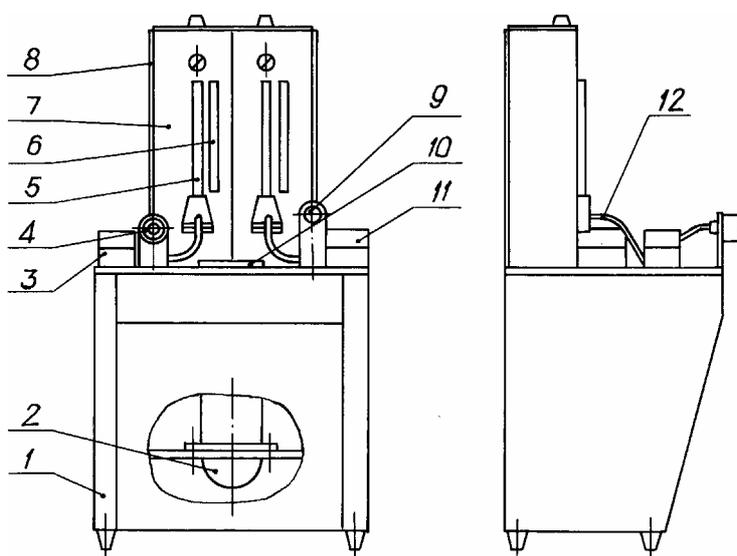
Схема пневматического измерительного стенда: 1 – корпус; 2 – баллон; 3 и 11 – стабилизаторы давления; 4 и 9 – пневматические калибры; 5 – стеклянная трубка; 6 – шкала; 7 – панель; 8 – щиток; 10 – плита; 12 – трубка воздушная
